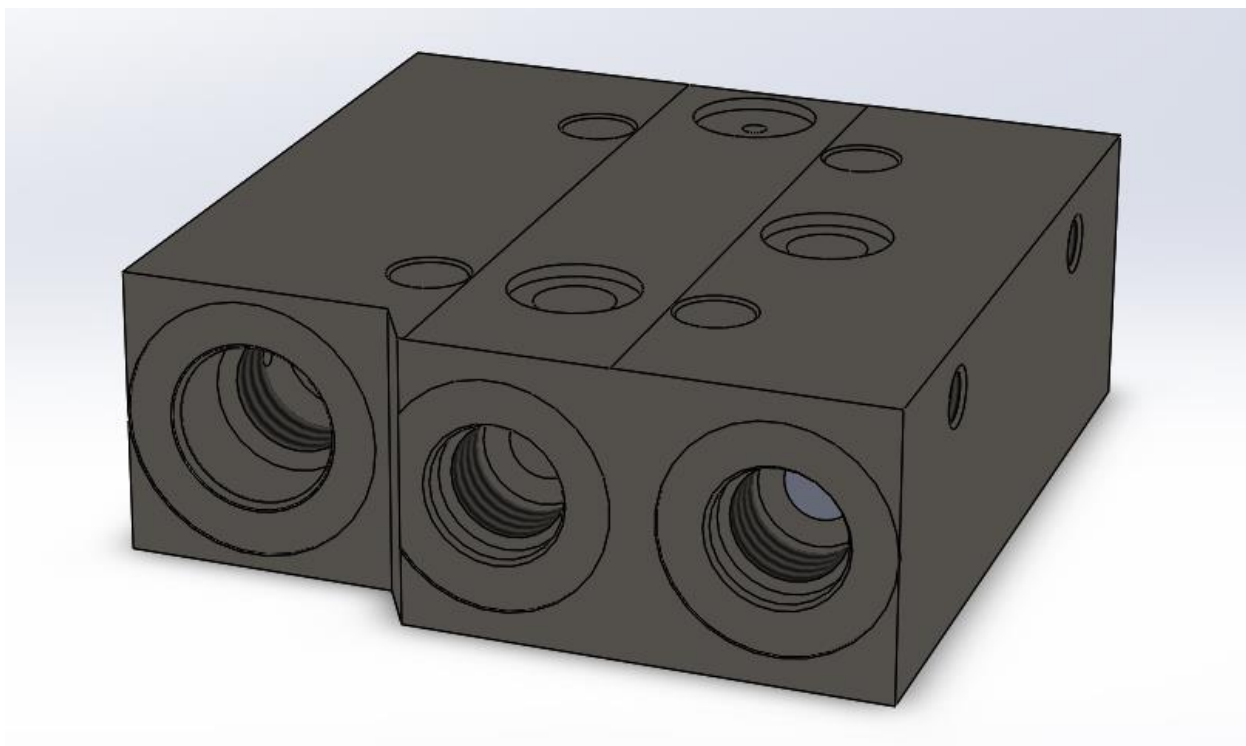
3-D модель деталі «Корпус клапанної секції»
